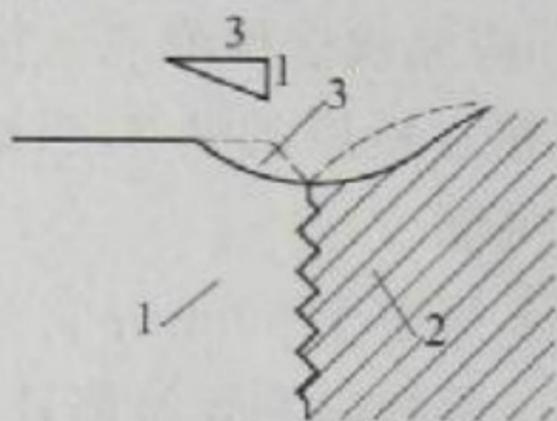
焊缝两侧的焊接缺陷用砂轮修磨示意
